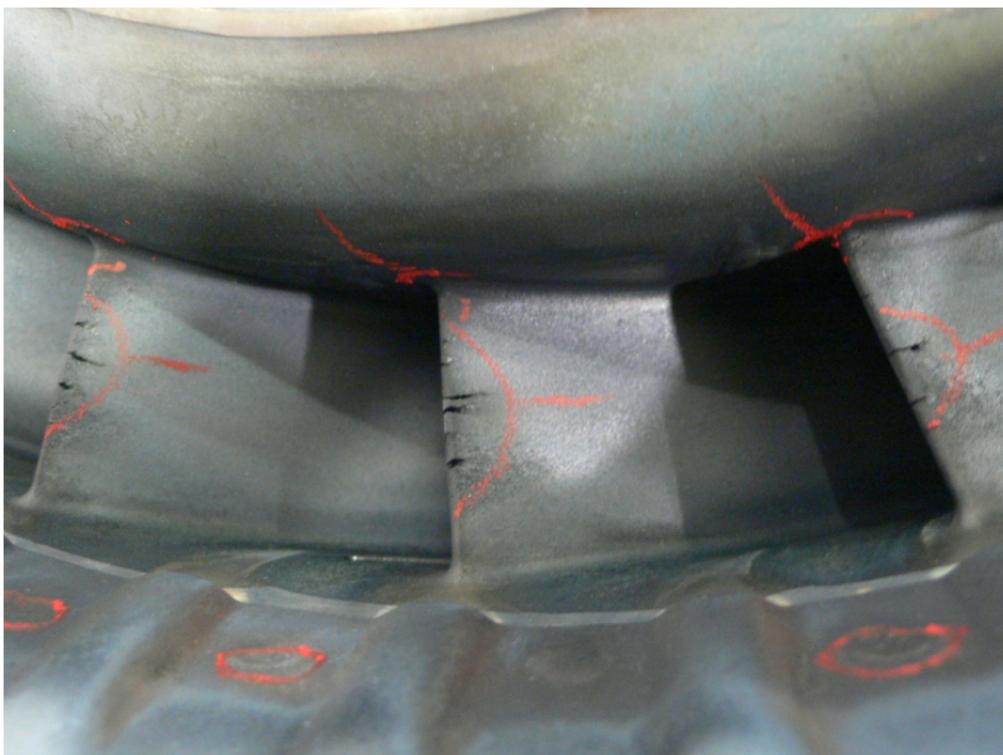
11-17 第 1 段固定翼前縁部のひび割れ
